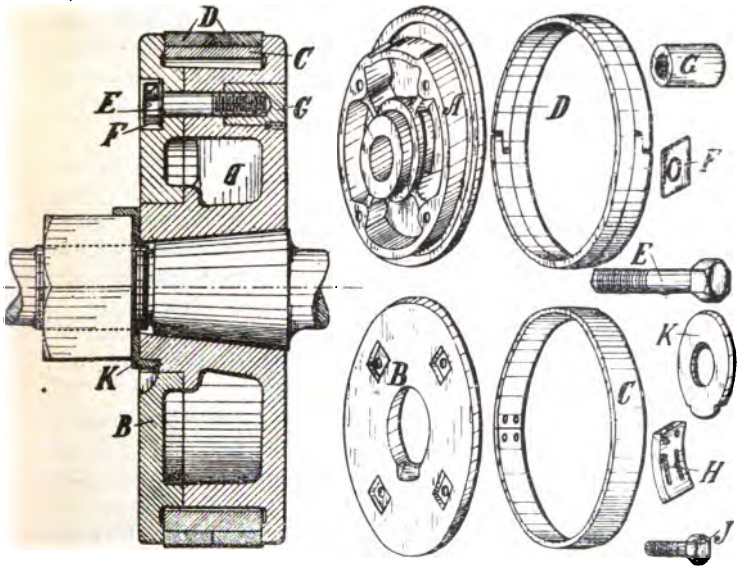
168. Dampfkolben für Maschinen über 400 Cylinderdurchmesser.
